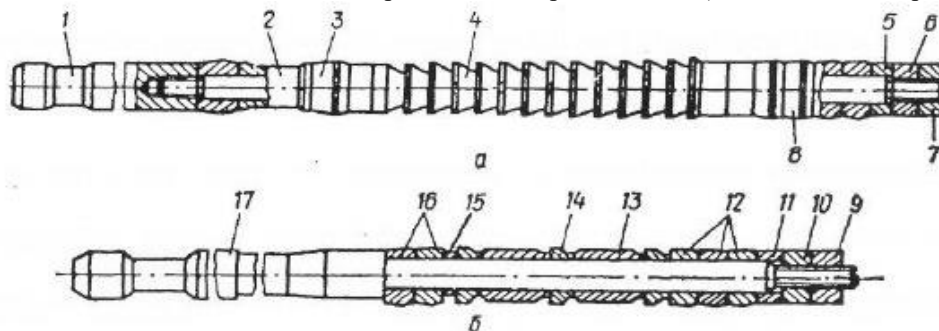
Деформуюче–різальна–деформуюча протяжка для обробки сталевих деталей (а) і деталей з кольорових сплавів (б) [2]
